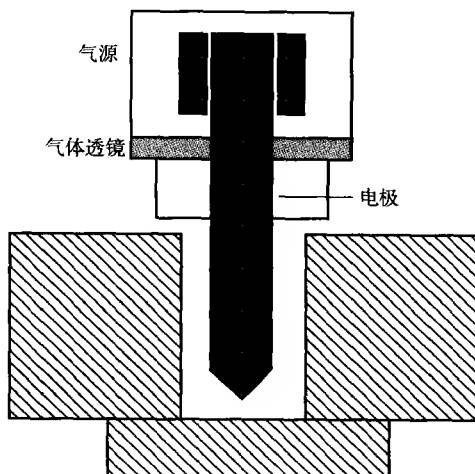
用传统 GTAW 焊枪进行的窄间隙焊
